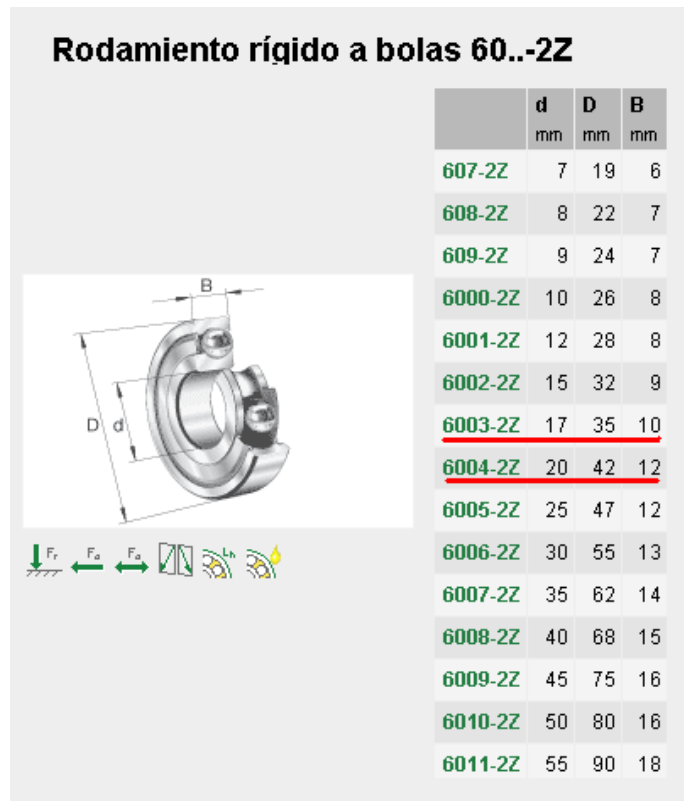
Selección de rodamientos Medidas principales según DIN 625-1.
